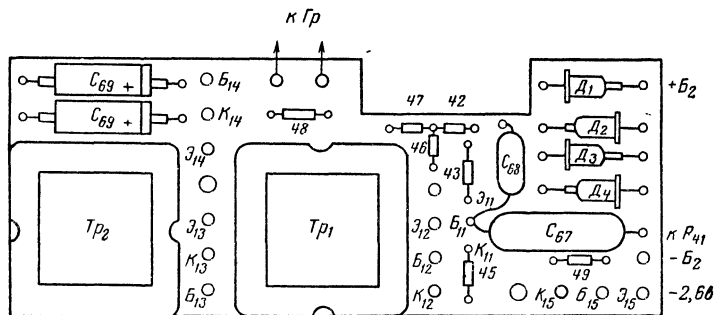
Блок усилителя низкой частоты и стабилизатора напряжения схемы на рис. 2.
